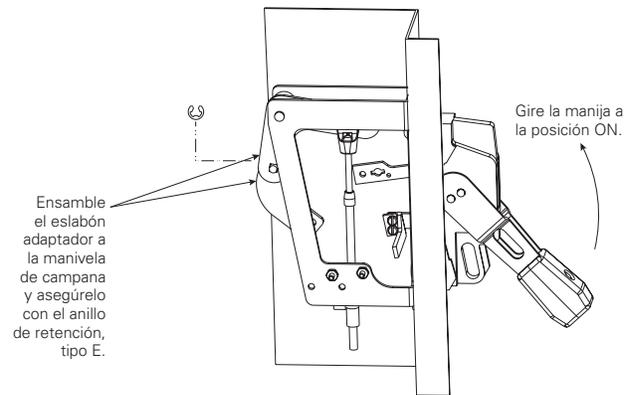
Ensamble de eslabón adaptador para manivela de campana
